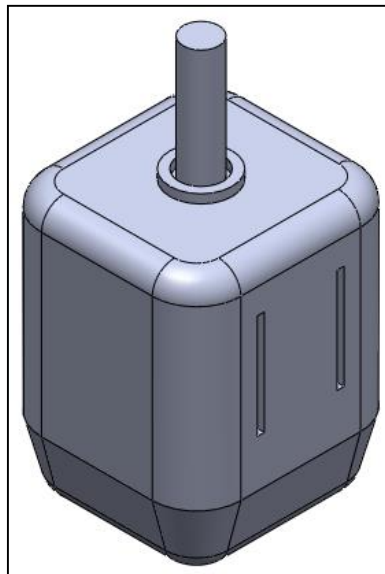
El motor DC de la M.C.V. ensamblado en SolidWorks.
